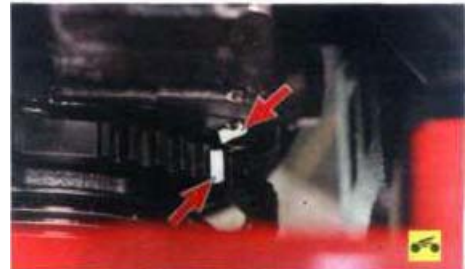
Установочные метки на зубчатом шкиве распределительного вала и задней крышке ремня привода газораспределительного механизма: 1 - шкив распределительного вала; 2 - задняя крышка привода газораспределительного механизма; 3 - метка на задней крышке; 4 - метка на шкиве
